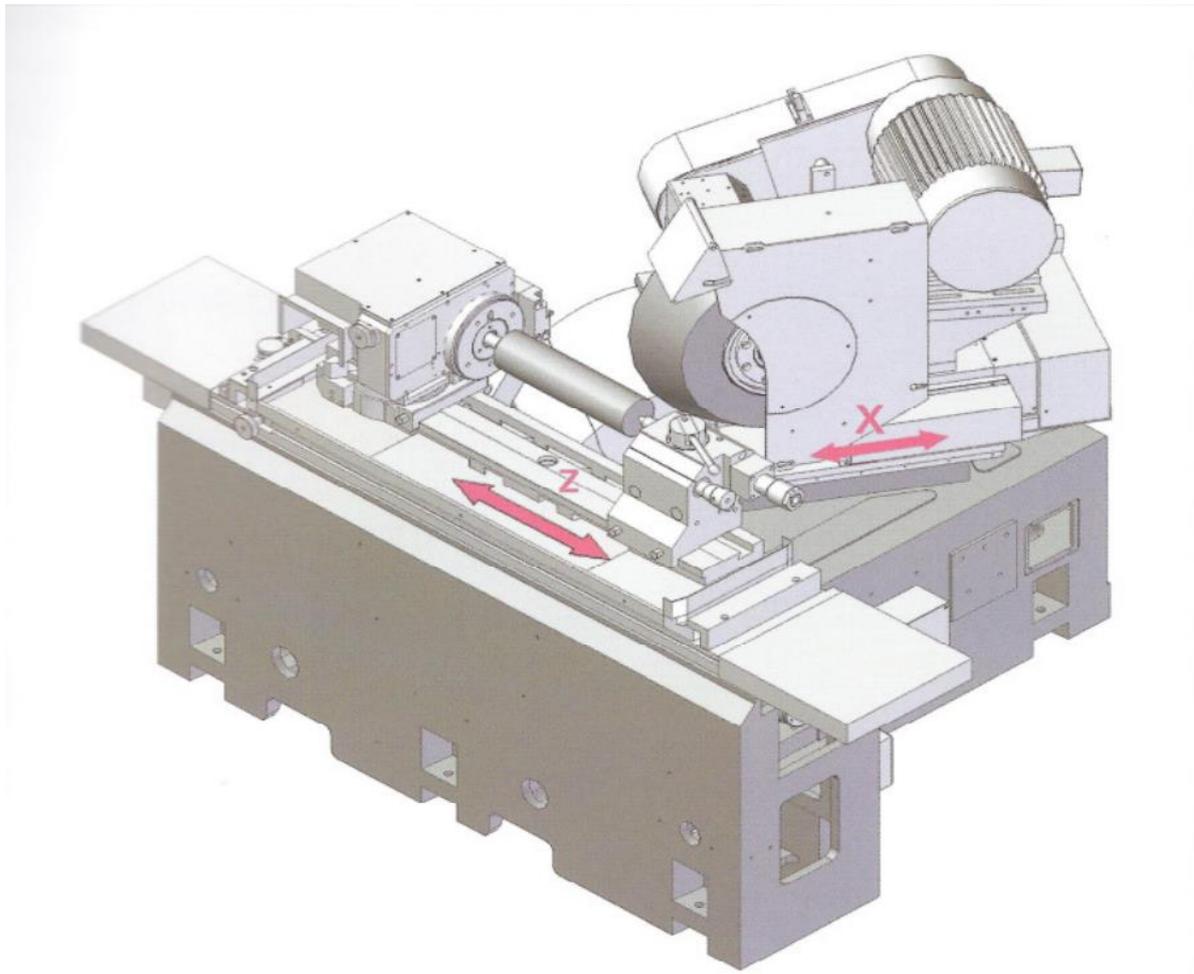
Aasi Schrägeinstich - Rundschleifmaschine^[6]
